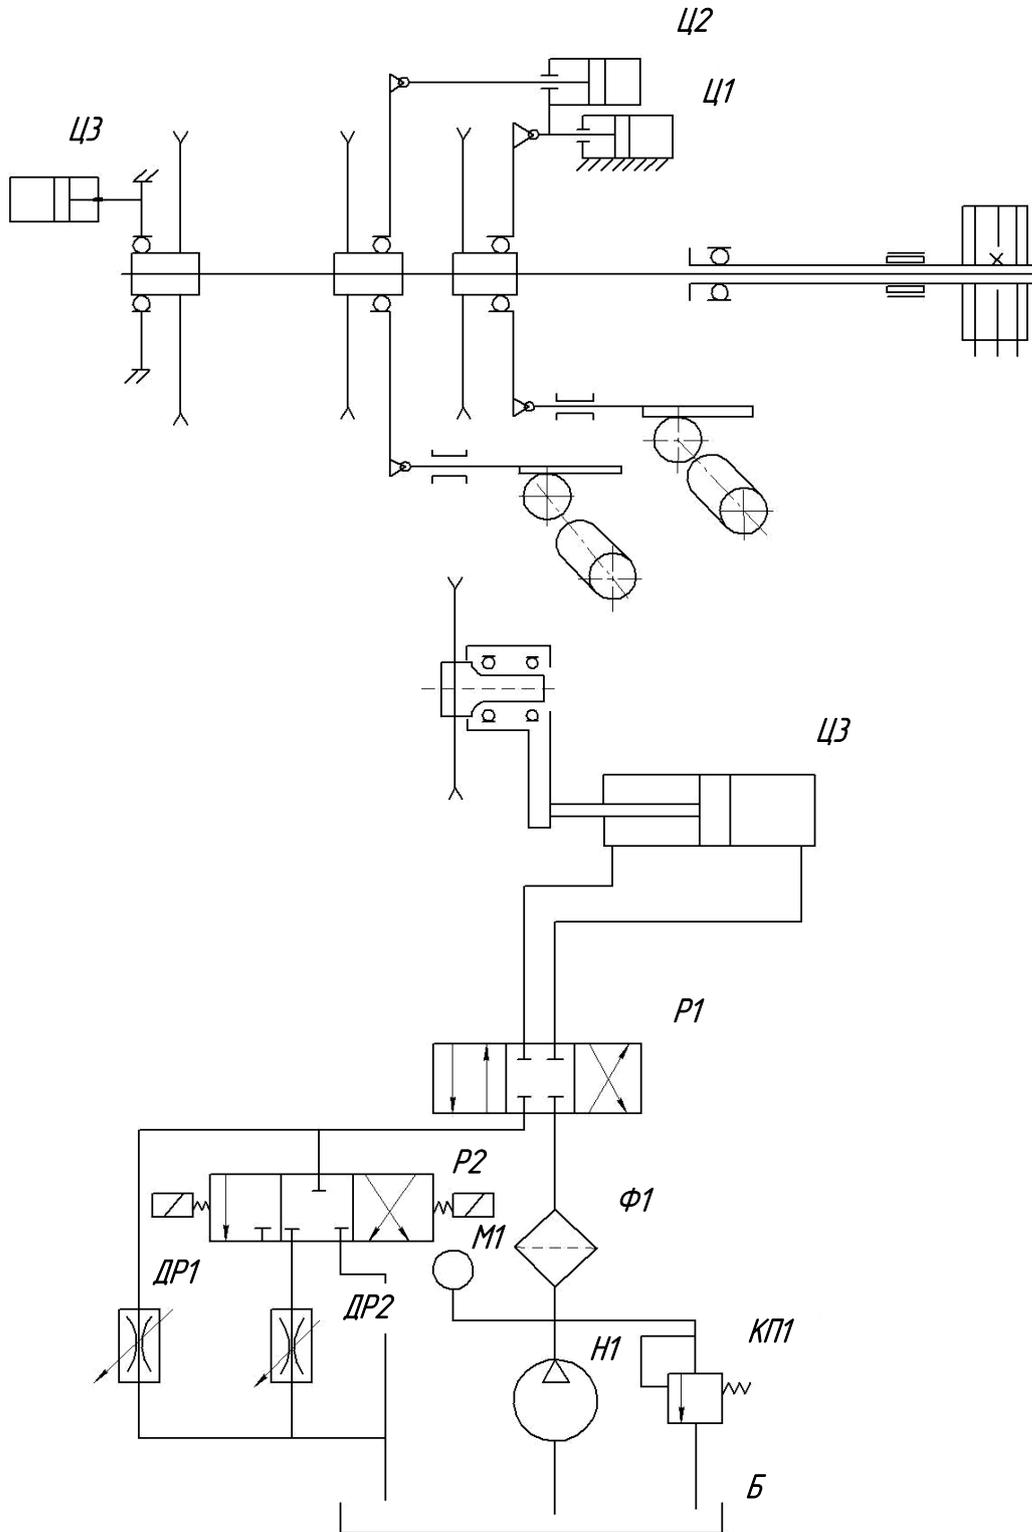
Гидрокинематическая схема круглопильного станка ЦЗ-Д7
